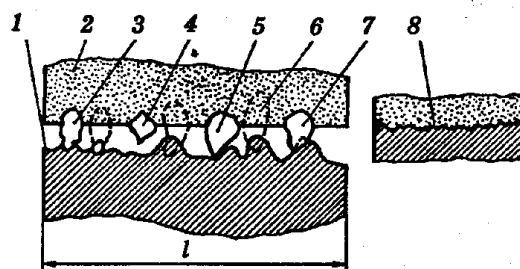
Схема образования шлифованной поверхности: 1 — шероховатая поверхность до шлифования; 2 — шлифовальный круг; 3, 4, 5, 7 — первый ряд абразивных зерен (сплошные линии), находящихся на одной образующей; 6 — второй (соседний) ряд зерен (штриховые линии); 8 — профиль шлифованной поверхности после выхода ее из зоны контакта с кругом
